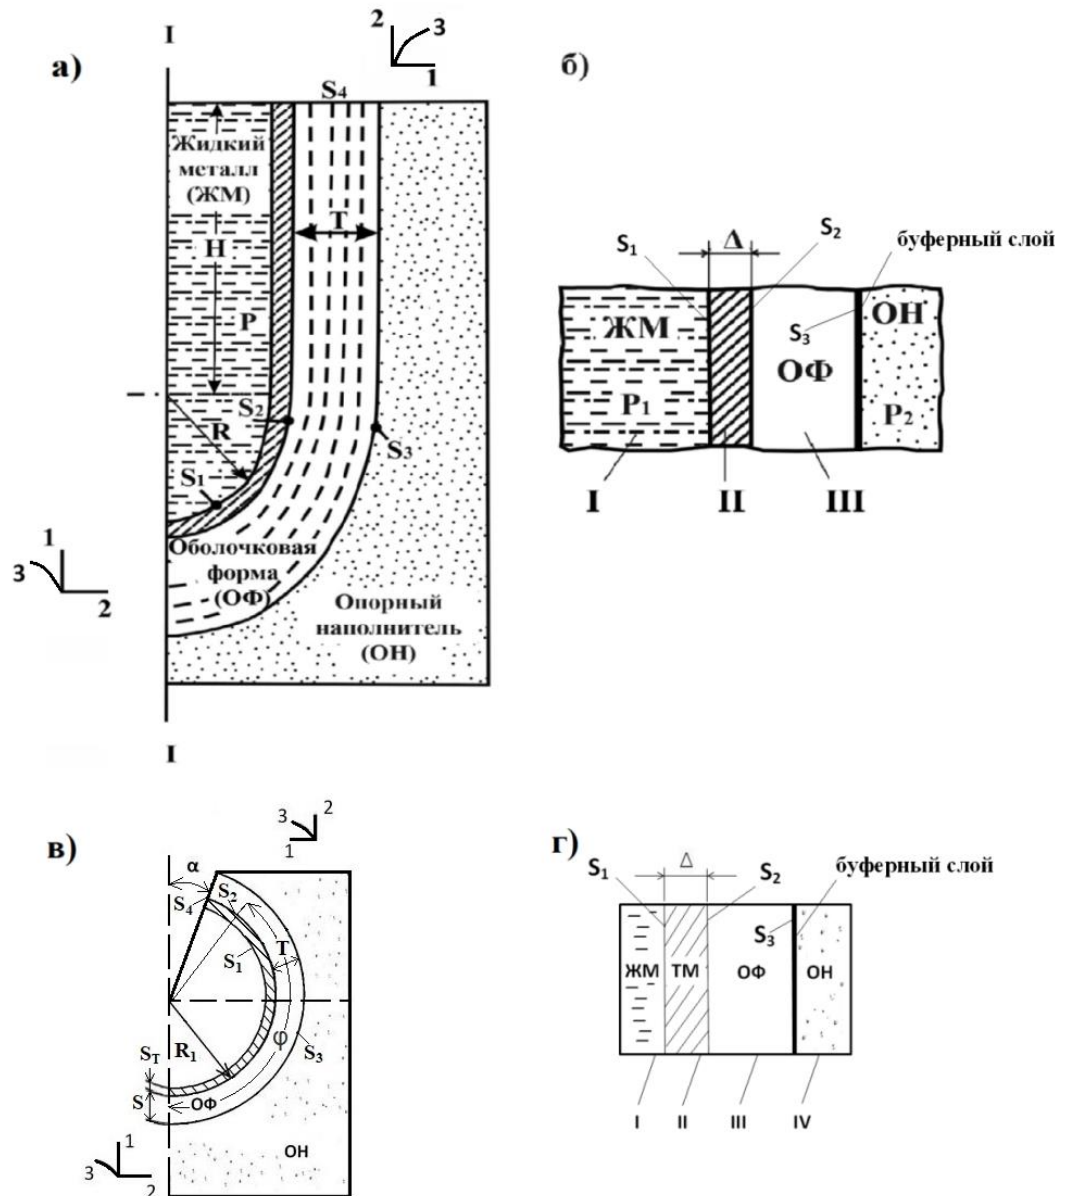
Расчетная схема оболочковой формы, заформованной в опорный наполнитель и залитая жидким металлом: а – сечение в вертикальной плоскости; б – схема моделирования областей системы «отливка – оболочковая форма – опорный наполнитель» с поверхностями к граничным условиям задачи I – жидкий металл, II – затвердевший металл, III – многослойная оболочковая форма, IV – опорный наполнитель; I-I – ось симметрии формы,  $S_1$  – внутренняя поверхность контакта жидкого и затвердевшего металла,  $S_2$  – поверхность затвердевшего металла и формы,  $S_3$  – внешняя поверхность формы,  $S_4$  – верхняя кромка стояка формы,  $T$  – толщина оболочковой формы,  $R$  – радиус сферической части цилиндрического стояка,  $R_1$  – радиус отливки,  $P$  – гидростатическое давление жидкого металла
